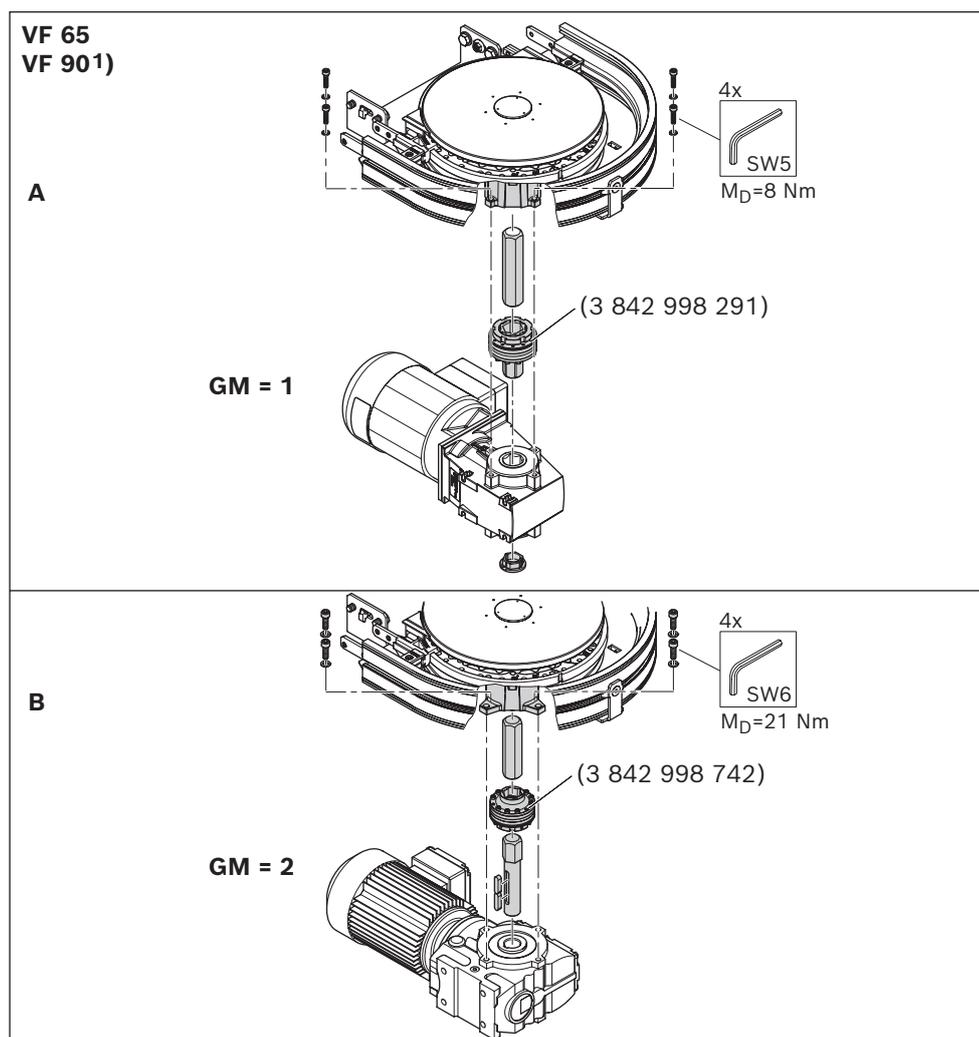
Montaje del accionamiento por ruedas de curva, motor reductor
